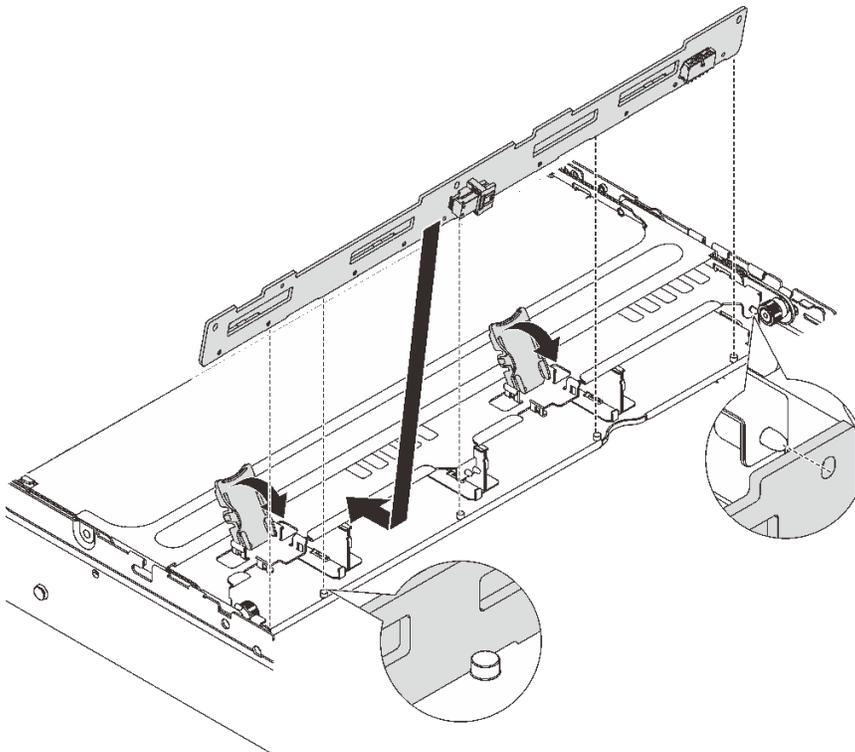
Installation du fond de panier d'unité 3,5 pouces central
